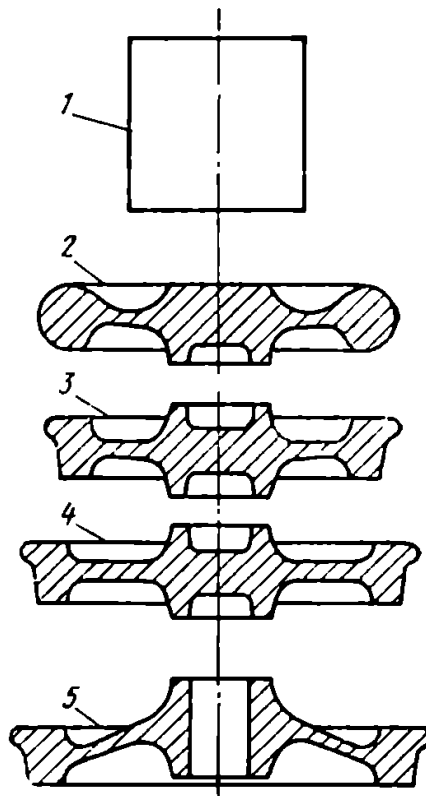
Схема формоизменения заготовки при производстве цельнокатаного железнодорожного колеса: 1 – заготовка; 2 – заготовка после предварительной штамповки; 3 – заготовка после окончательной штамповки; 4 – заготовка после прокатки; 5 – заготовка после выгибки диска, калибровки колеса и прошивки отверстия
